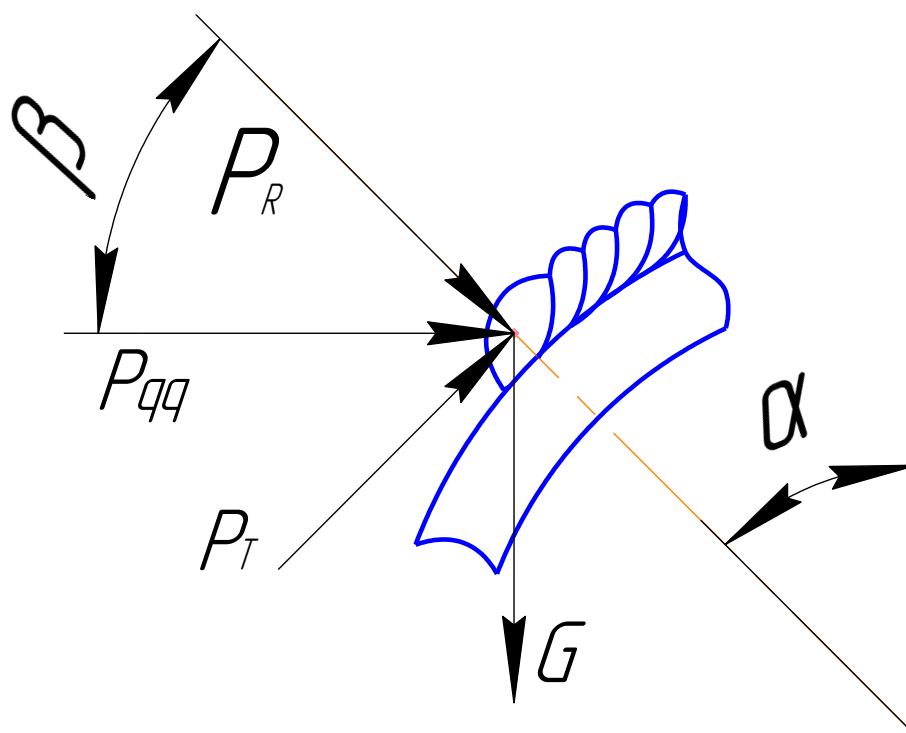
Схема действия сил на сварочную ванны при сварке на “спуск” в положении $\alpha=0\div 90^0$.
